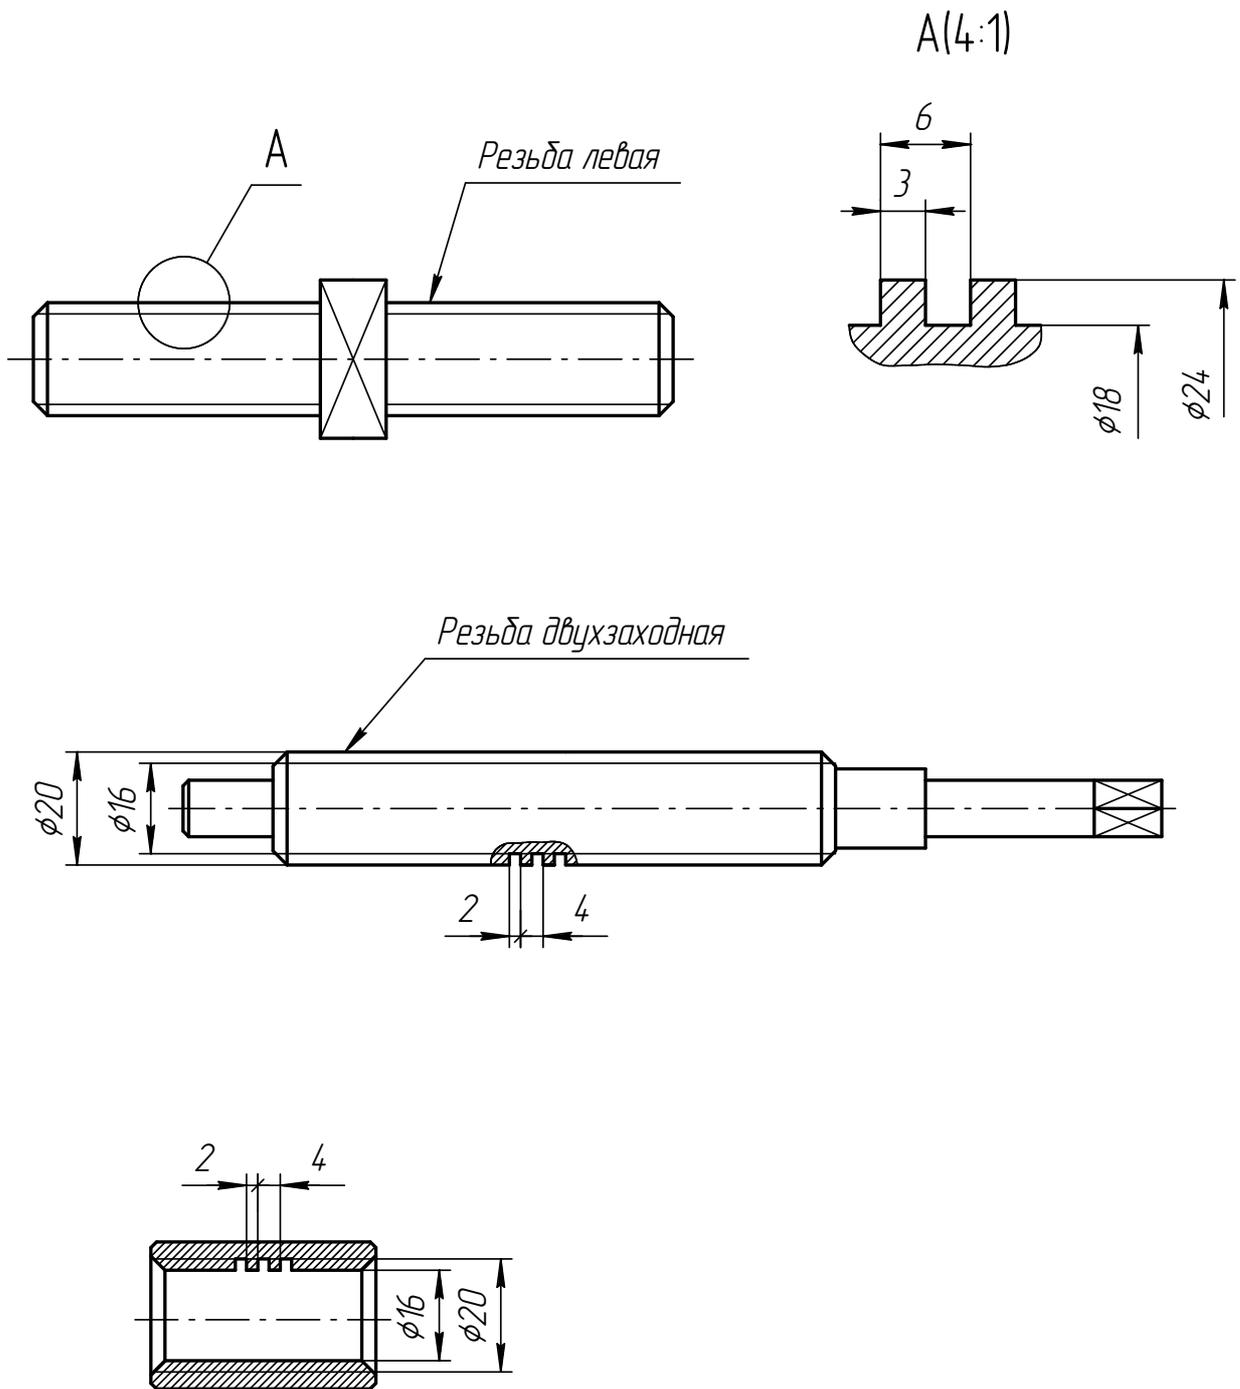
б – Простановка размеров прямоугольной резьбы на чертежах
